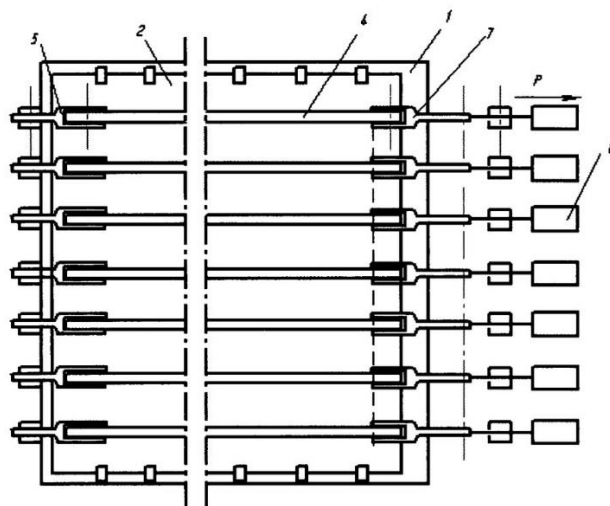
Схема закрепления и установка ребра жесткости на настильный лист в стенде (вид сверху)
